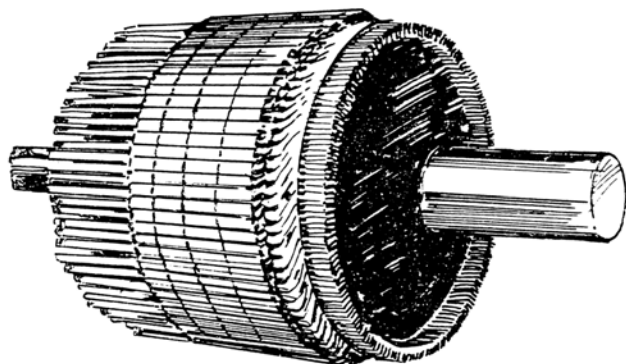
BOBINADO DE BARRAS DE UN ROTOR DE MOTOR TRIFÁSICO.
